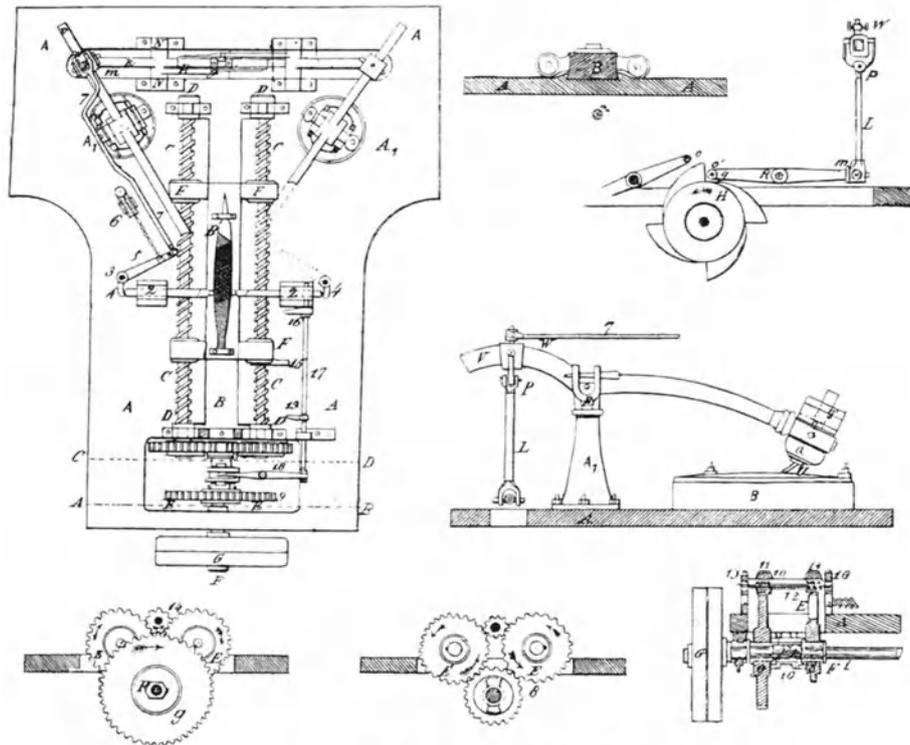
Englische Haumaschine „Stocker“, 1836.
